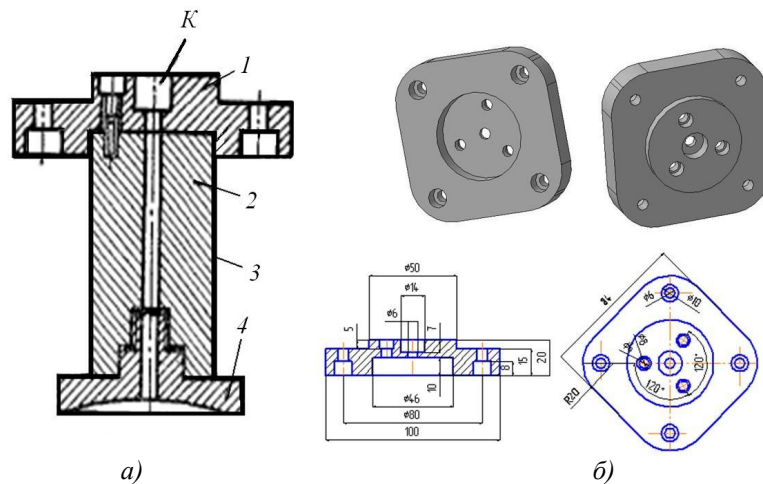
Сборный электрод-инструмент и заготовка алюминиевой детали с покрытием чугуном:
